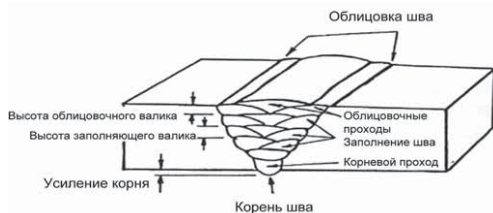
Корень шва является первым или самым нижним проходом при сварке в несколько проходов
